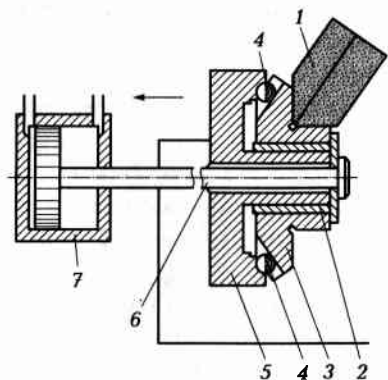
Схема обработки поверхностей круглым наружным шлифованием с угловым расположением шлифовального круга
